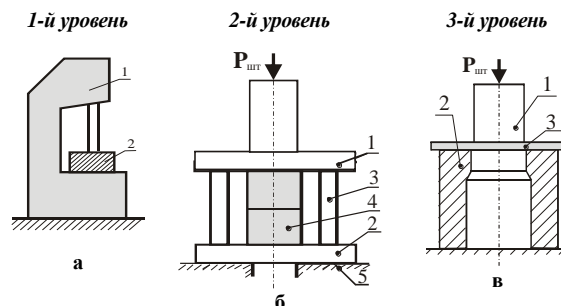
Подсистемы технологической системы "пресс – штамп – режущие части – заготовка":
